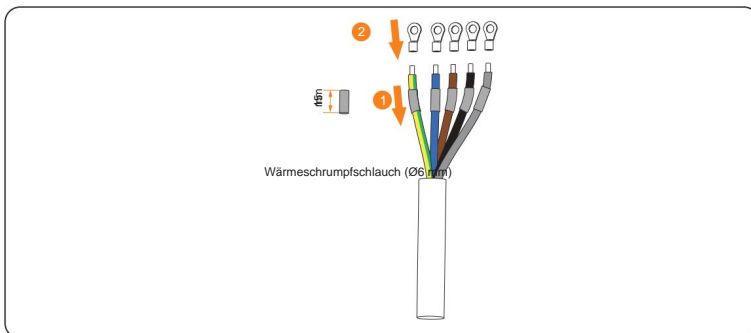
Installation der Schläuche und des R-Anschlusses
